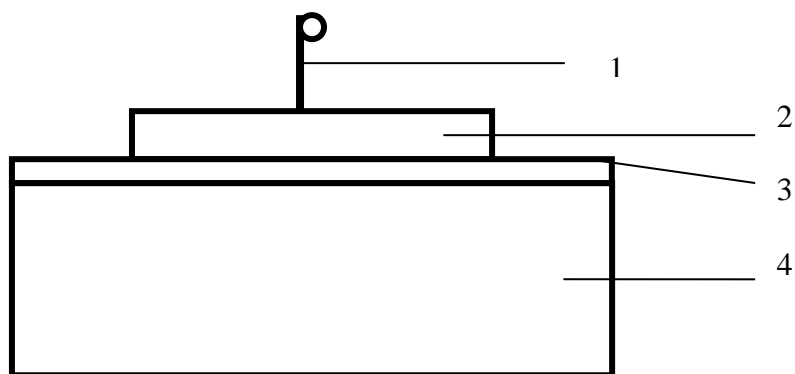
Общее устройство редуктора: 1 – рычаг включения; 2 – механизм исключения; 3- крышка; 4 – корпус.
